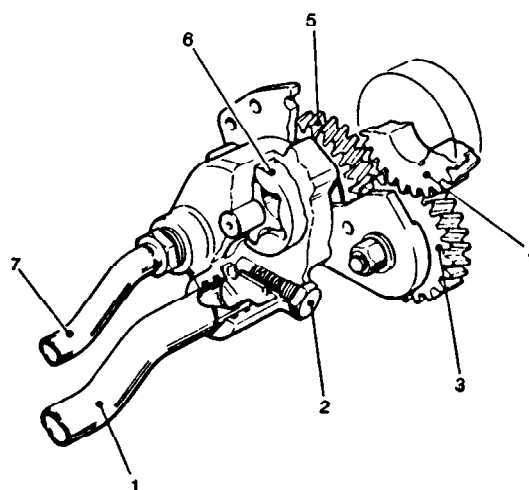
Bomba de aceite tipo de rotor: 1 entrada, 2 válvula de desahogo, 3 engrane intermedio, 4 engrane del cigüeñal, 5 engrane de mando, 6 rotores, 7 salida
